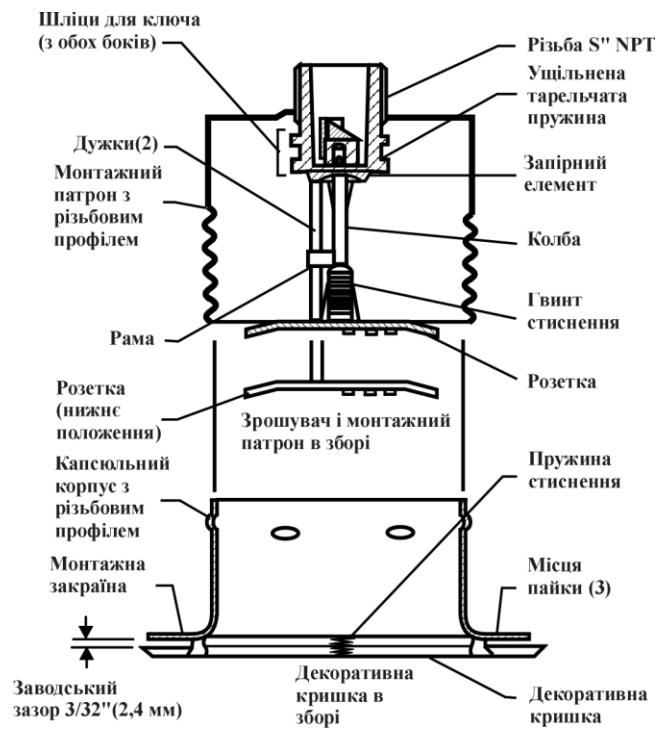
Спринклерний зрошувач таємний, стандартного реагування розеткою до низу (для установки під підвісну стелю)
